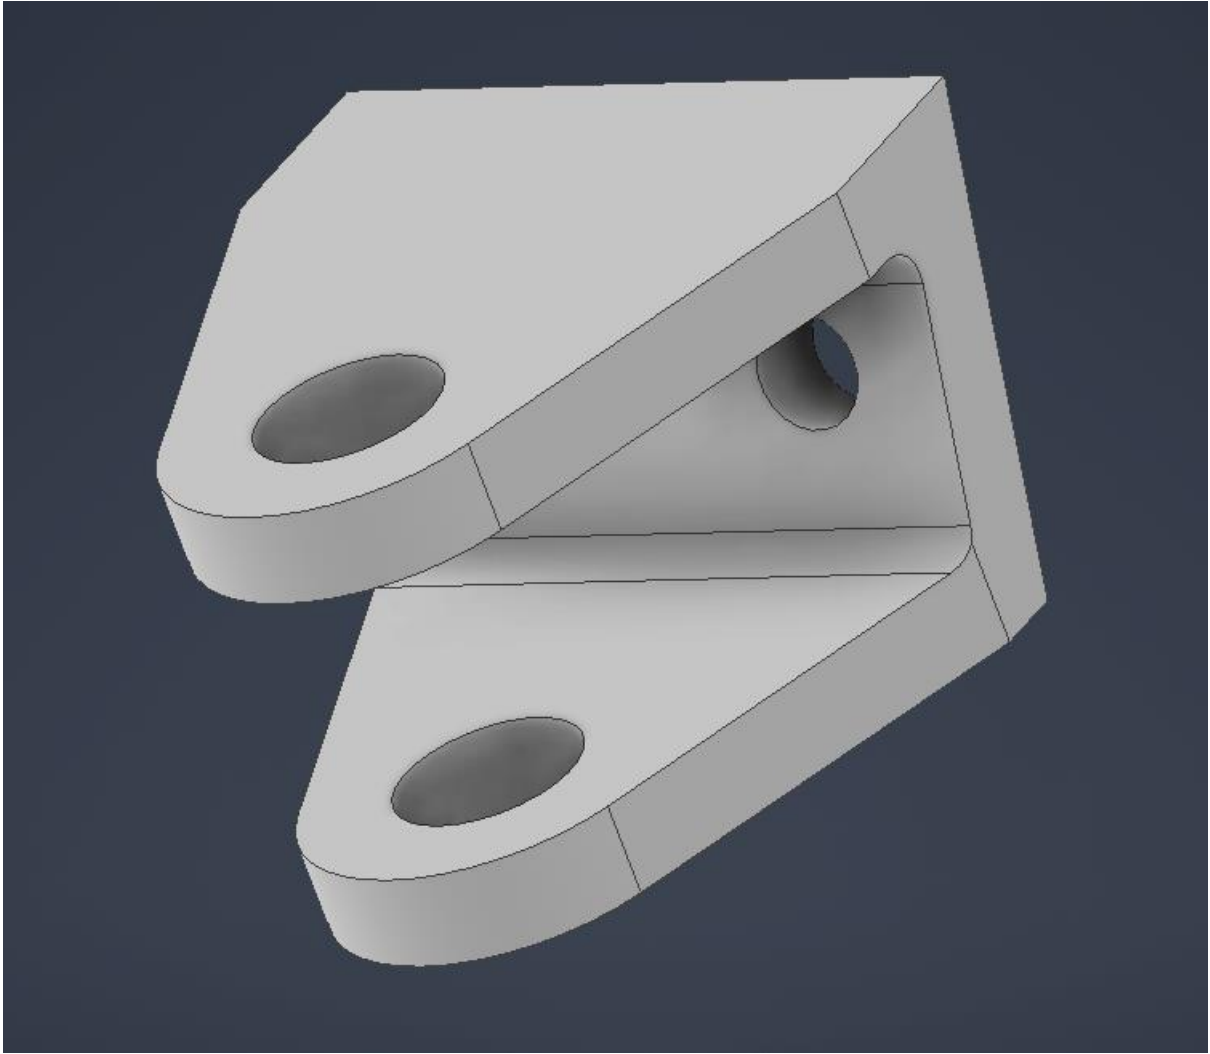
Bolteforbindelser mellom spindel og braketter.
